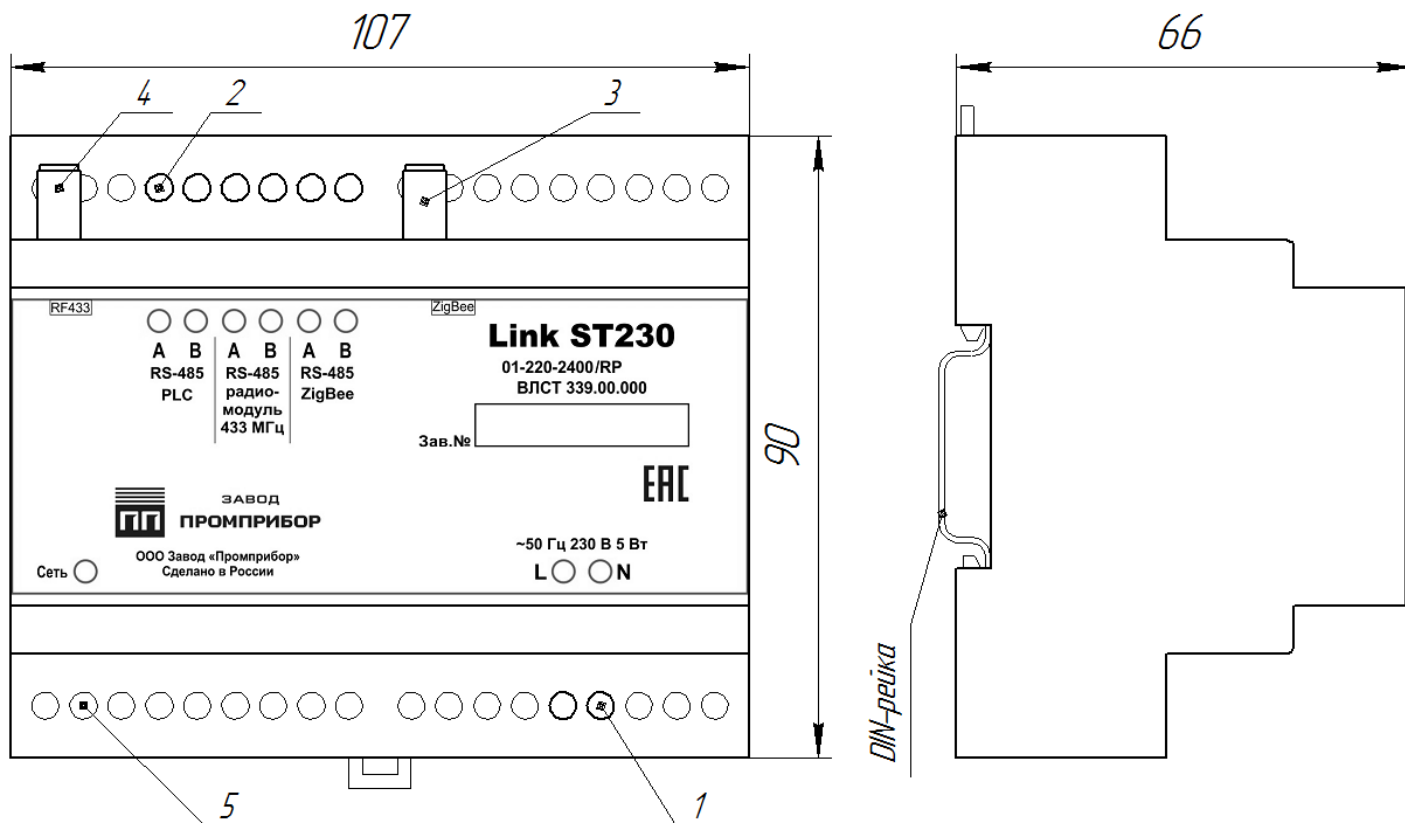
Внешний вид и размеры модема в исполнениях ST200-01-xxx-0433-2400-SMA и ST230-01-xxx-xxxx/xx-SMA
